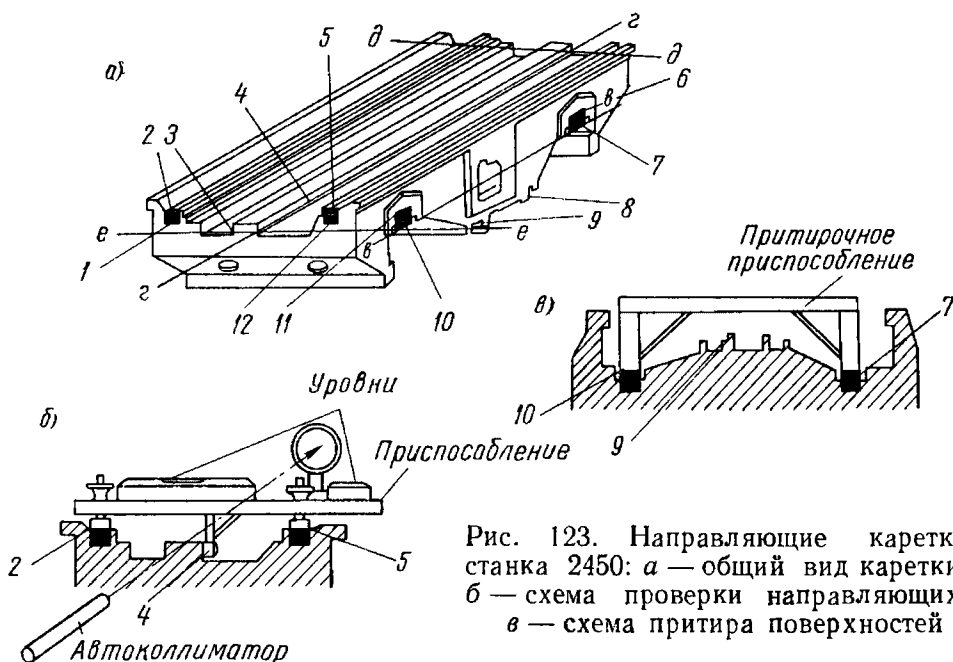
Направляющие каретки станка 2450: а — общий вид каретки; б — схема проверки направляющих; в — схема притира поверхностей
